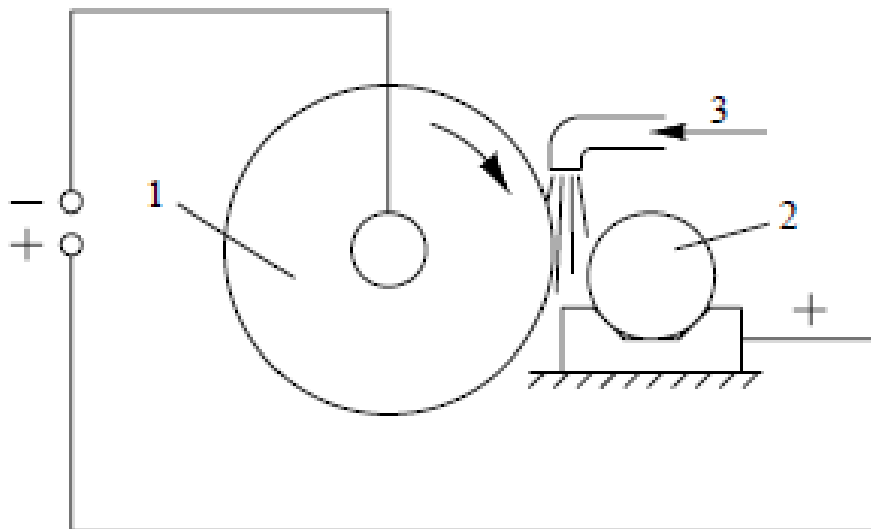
Princip zařízení pro elektrokotaktní obrábění [16]
